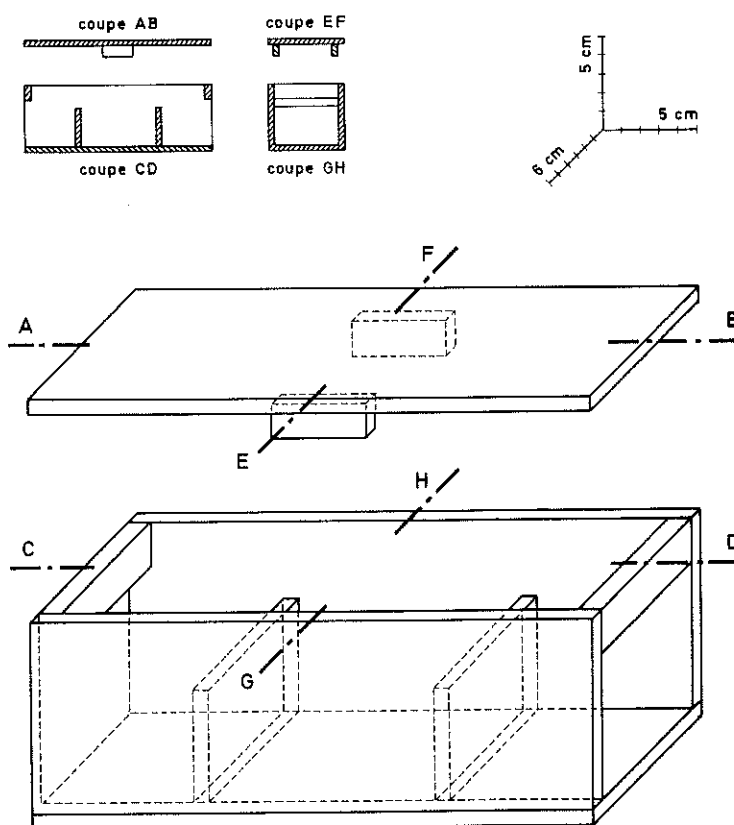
Plan d'une boîte à appâts convenant bien pour le surmulot..
